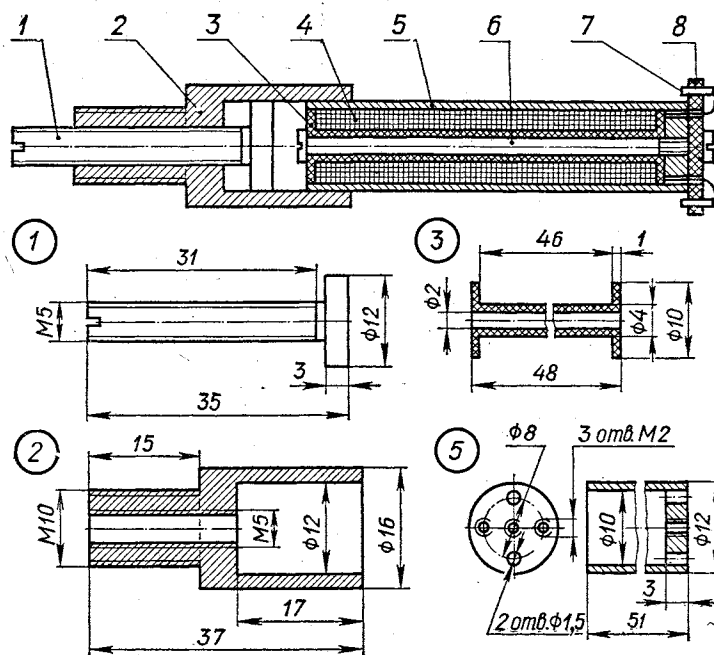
Компенсирующее устройство: 1—подстроечный сердечник, Ст.3; 2—корпус, ЛС59-1; 3—каркас катушки, эбонит; 4—обмотка; 5—стакан, Ст.3; 6—винт; 7—контакт, проволока медная диаметром 1,6 мм, 2 шт., запрессовать в дет. 8; 8—пластина, гетинакс толщиной 1,5 мм, закрепить на дет. 5 двумя винтами М2×3.
